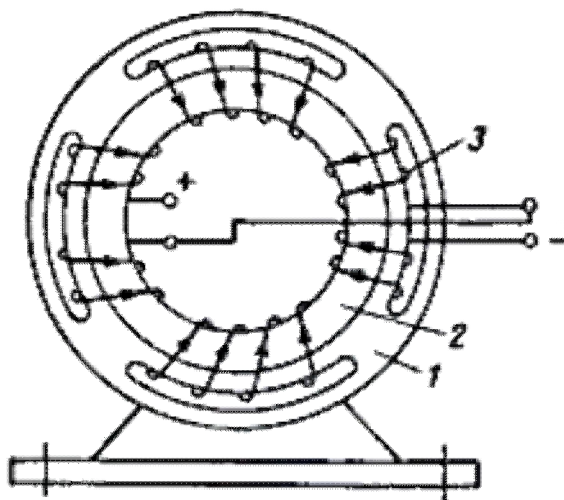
Принципова схема розташування обмотки підмагнічування спинки статора (1 – корпус машини, 2 – сердечник статора; 3 – обмотка підмагнічування)
